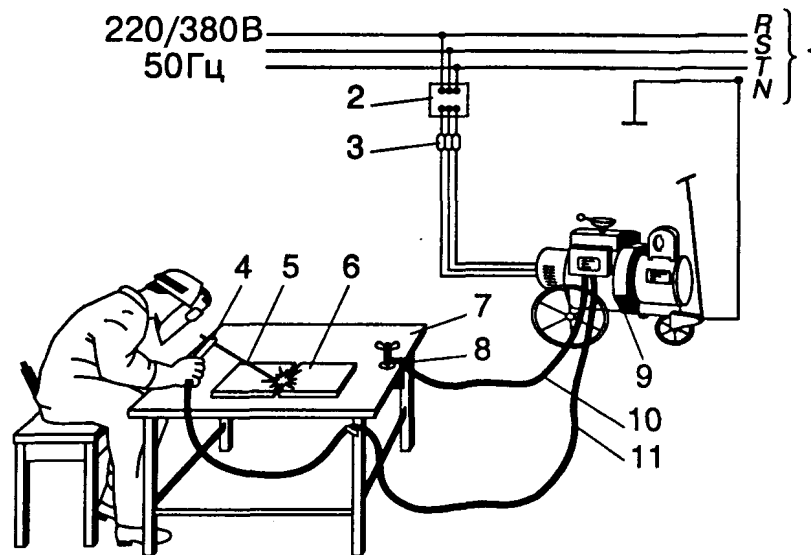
Обладнання робочого місця для дугового зварювання:
